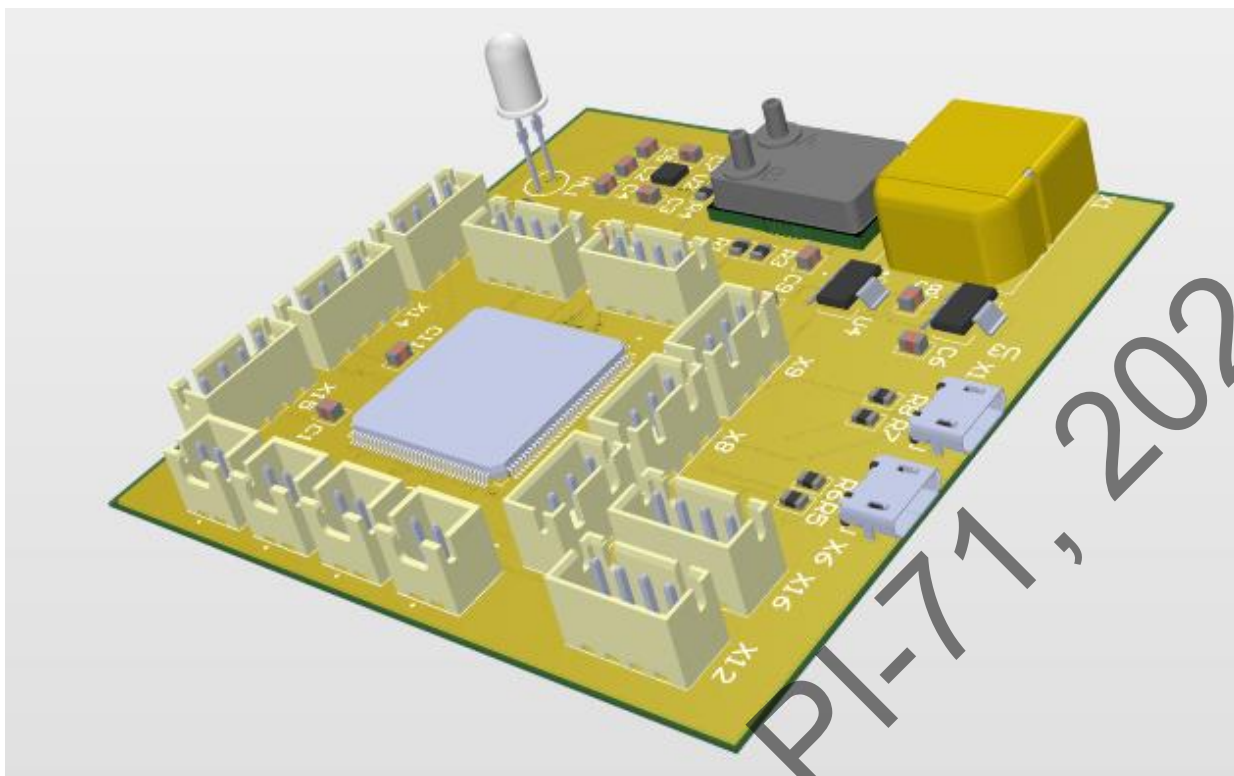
Тривимірна модель друкованої плати у середовищі Altium Designer PCB
